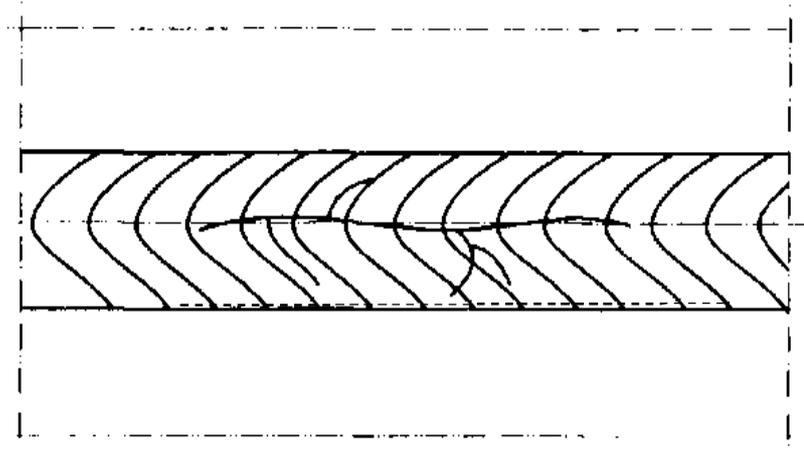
Разветвленная трещина сварного соединения
